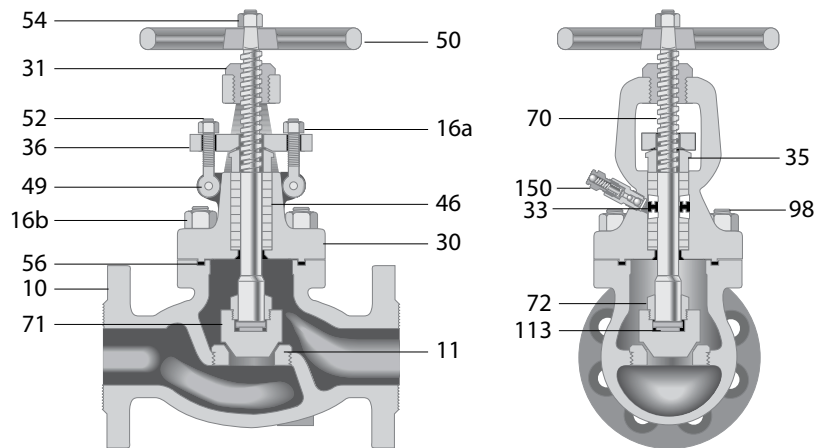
G-HF8T - GLOBO ALQUILACIÓN 300LBS BRIDAS UOP
